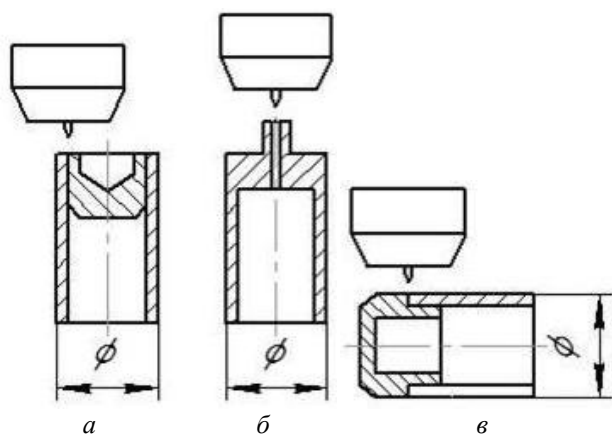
Конструкции сварных соединений герметизирующих узлов:
